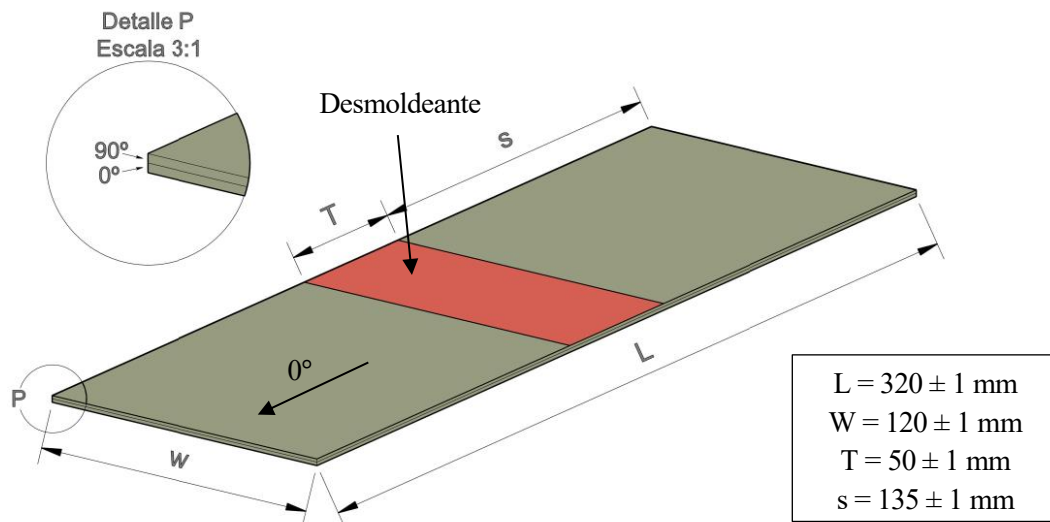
Apilado de la lámina desmoldeante central del panel 3
